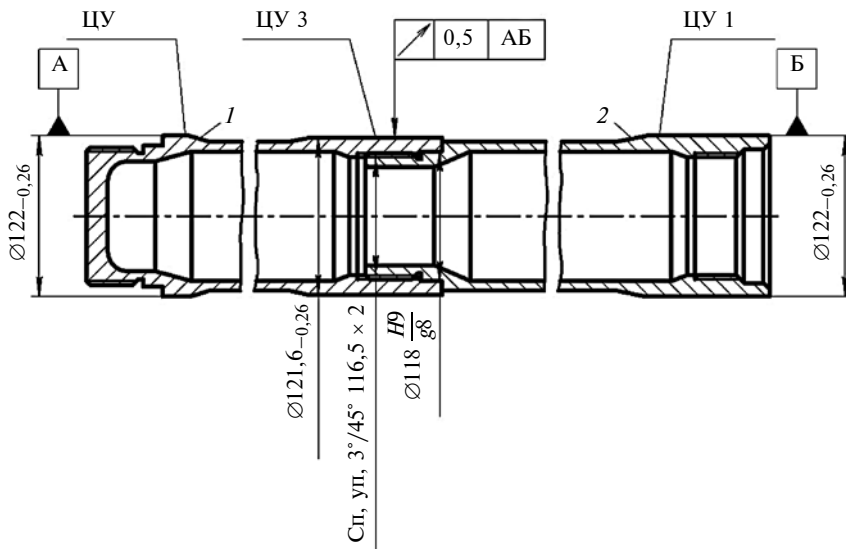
Сборный корпус ракетного двигателя с резьбовым соединением труб 1 и 2
